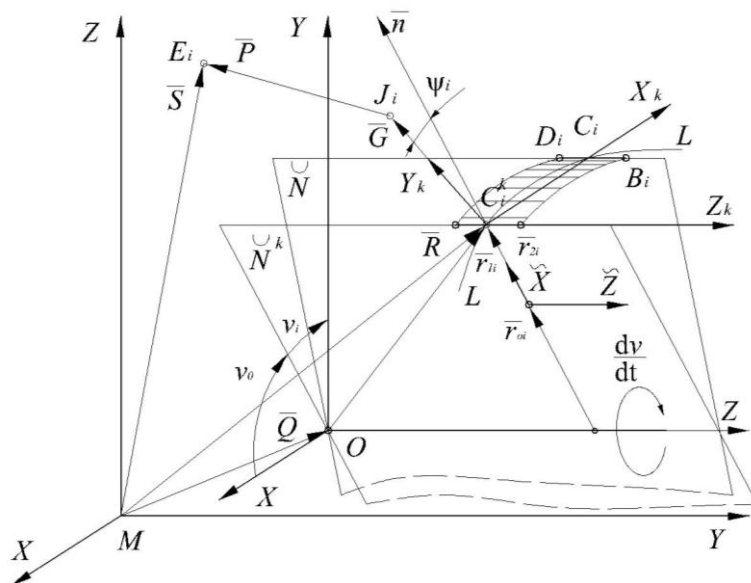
Розрахункова схема для визначення координат розміщення виконавчих органів верстату і точки контакту інструменту з поверхнею навивної заготовки в процесі її формоутворення
